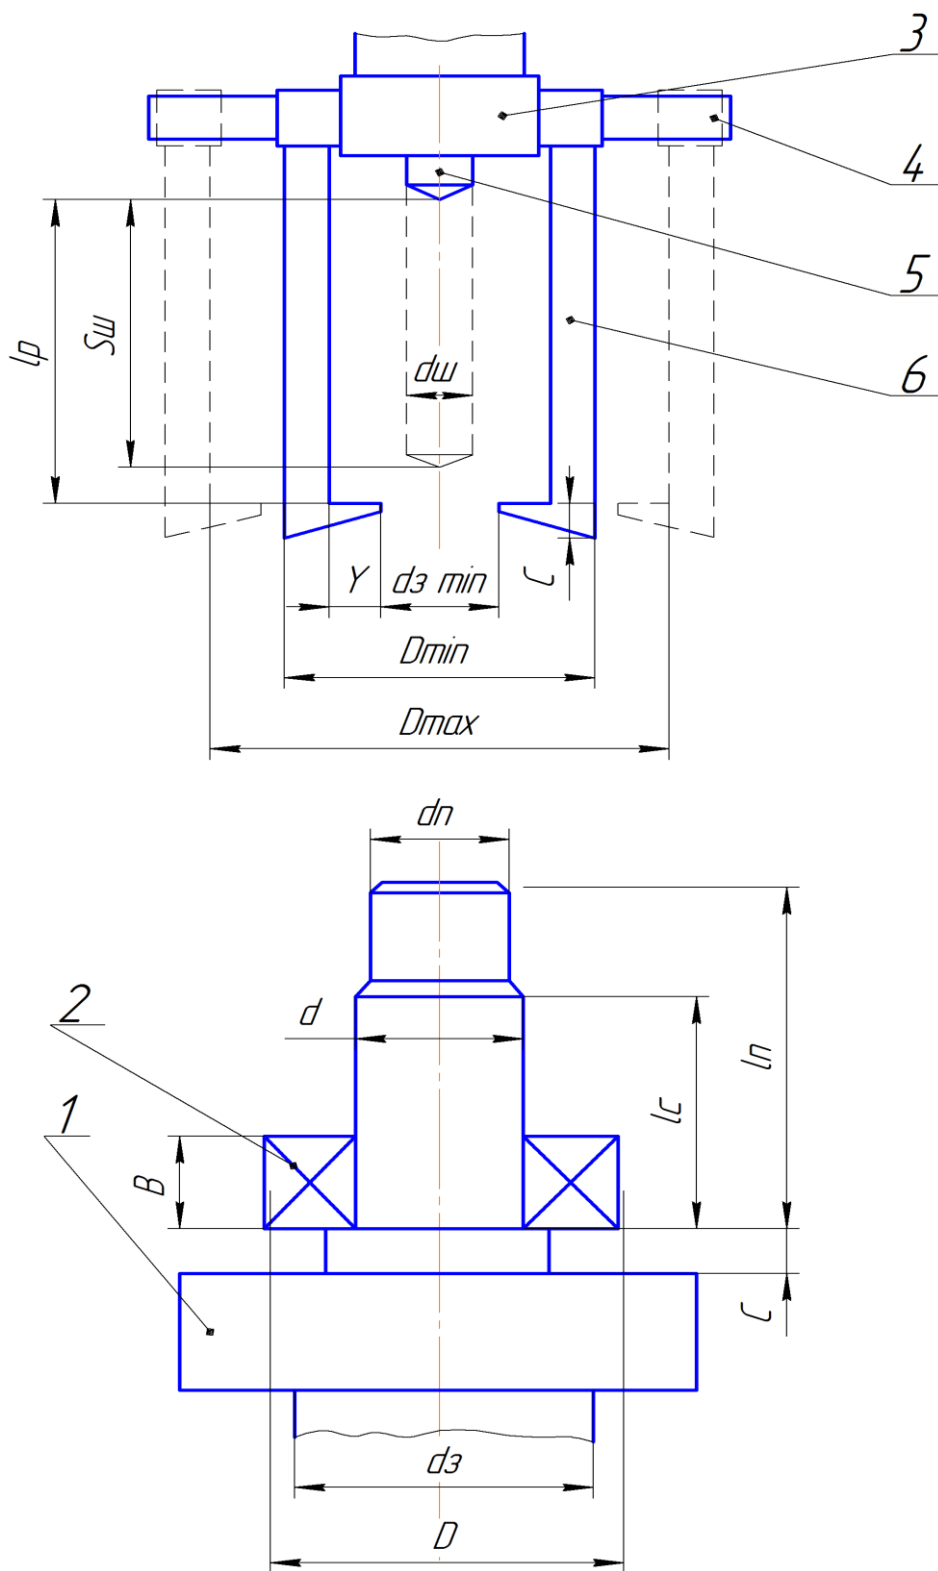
Схема для узгодження геометричних параметрів знімача з геометричними параметрами підшипникового вузла: 1 – вал; 2 – підшипник; 3 – силовий циліндр; 4 – траверса; 5 – шток; 6 – захоплювач.
